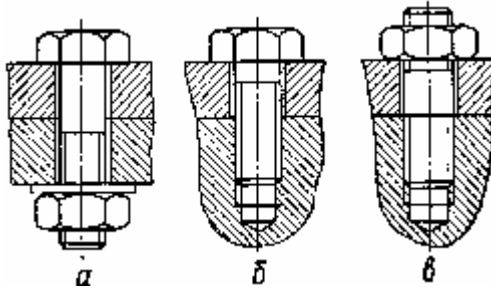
З'єднання за допомогою болта, гвинта та шпильки
